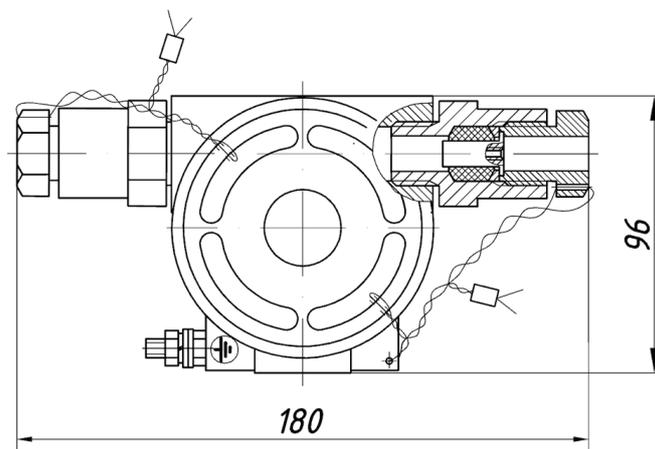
Габаритные размеры светозвукового Оповещателя Филлин -1К
